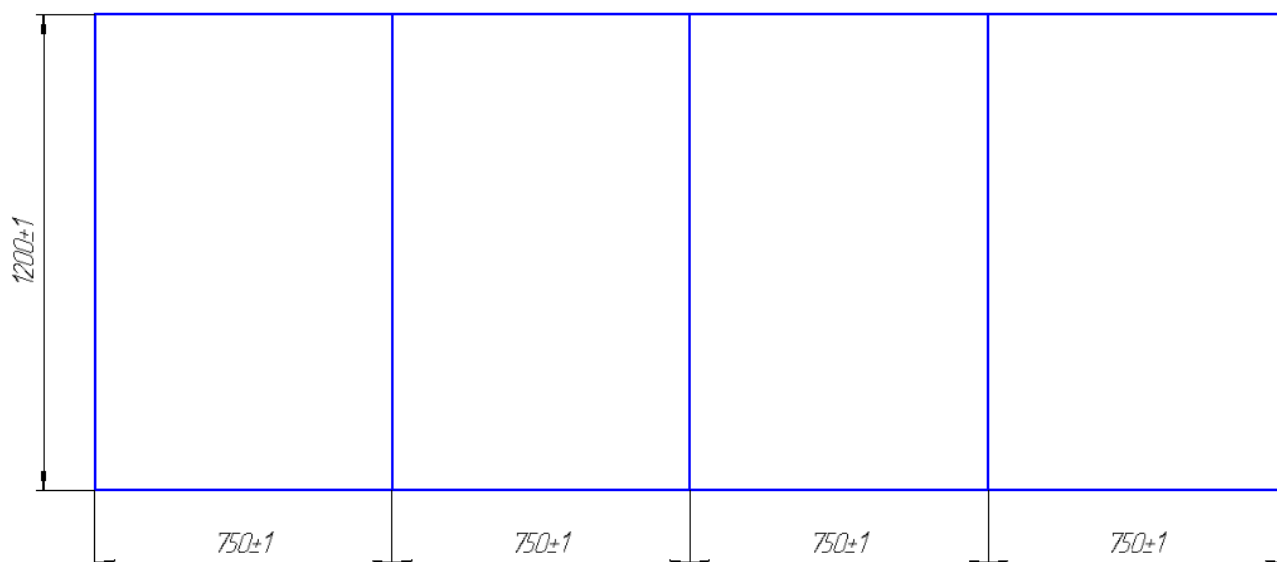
Схема роспуска листов при помощи установки плазменной резки
